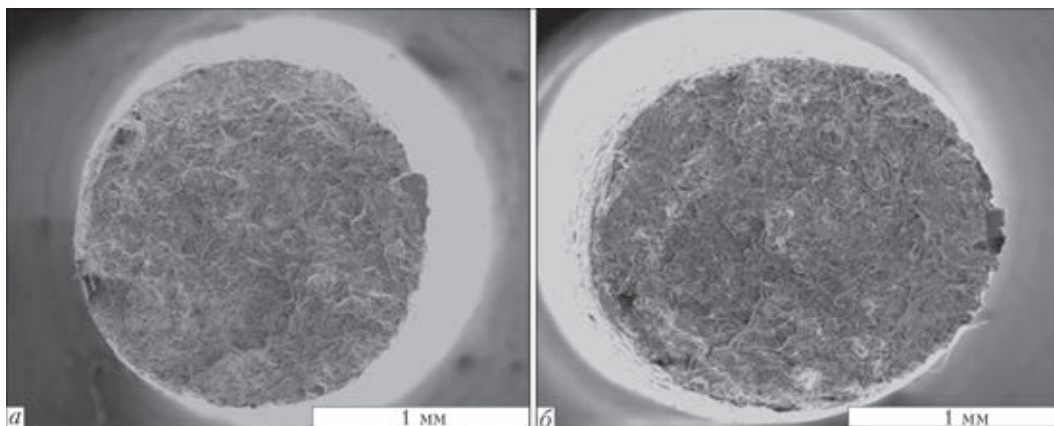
Макрофрактограммы поверхностей разрушений после испытаний на статическое растяжение: а — образец сварного соединения 1; б — образец 2 сплава технического титана ВТ1-0 ДШП толщиной 12 мм, упрочненного азотом (0,098 мас. %)
